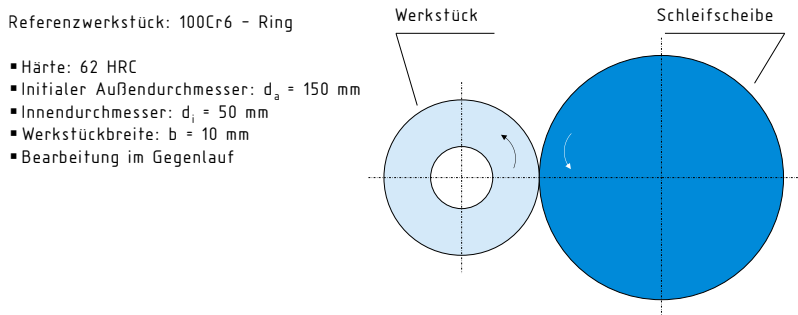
Initiale Dimensionen des Referenzwerkstücks
